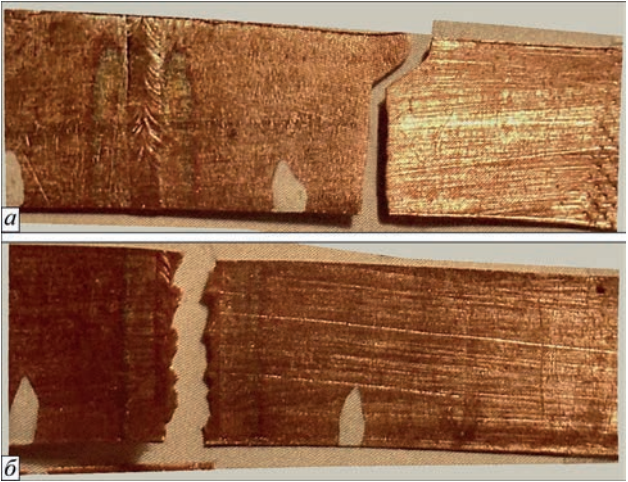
Характер механічних руйнувань зварних з’єднань після механічних випробувань на розрив: а – по основному металу; б – по лінії сплавлення зварного шва з основним металом
